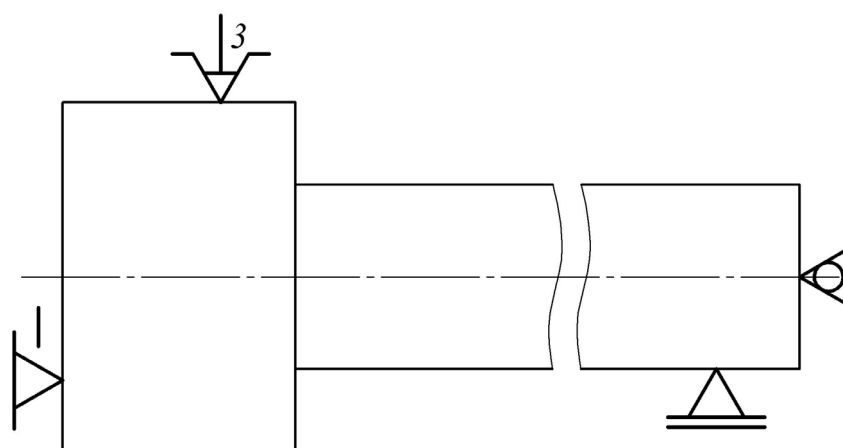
Приклад схеми установлення деталі типу вал
